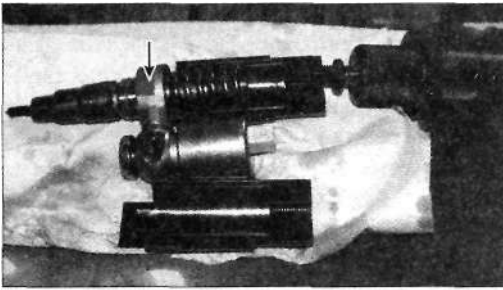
Демонтированная насос-форсунка с деталями специального приспособления для ее демонтажа (стрелкой показана одна из фрезерованных плоскостей, по которым фиксируется приспособление)
